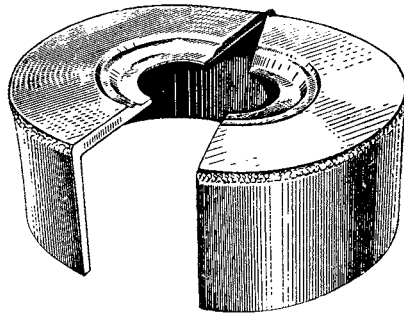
Приспособление 48001-1-123П для спрессовки шестерни дет. 237-15-62 и подшипника дет. КВ-15-19 с несущего диска бортовой передачи
